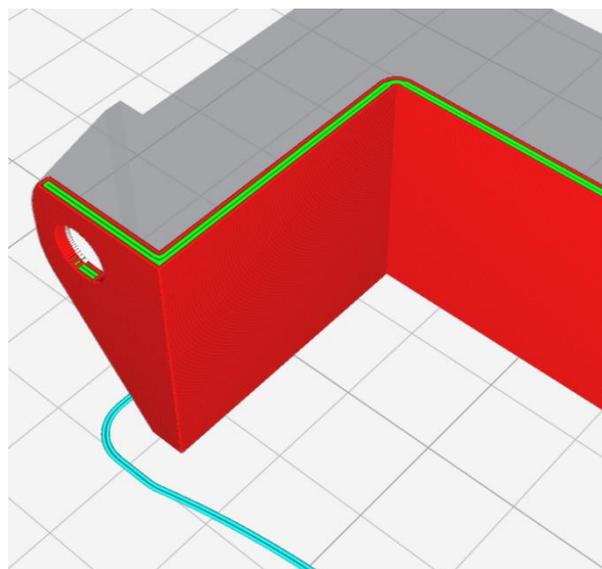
Держатель удлинителя со стенкой 1,6 мм
